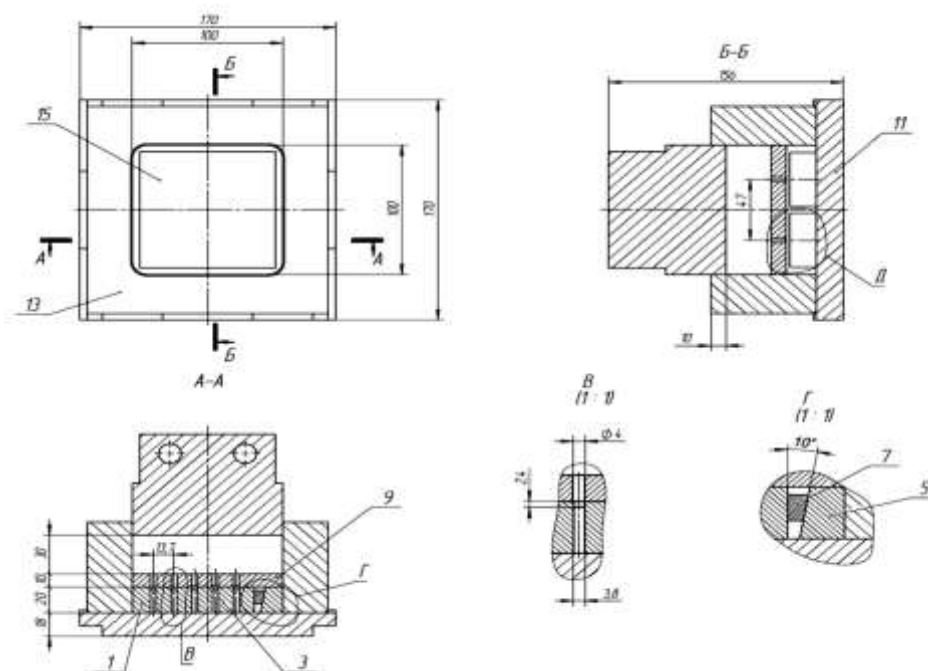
Чертеж технологической оснастки для пропитки заготовок под высоким давлением
